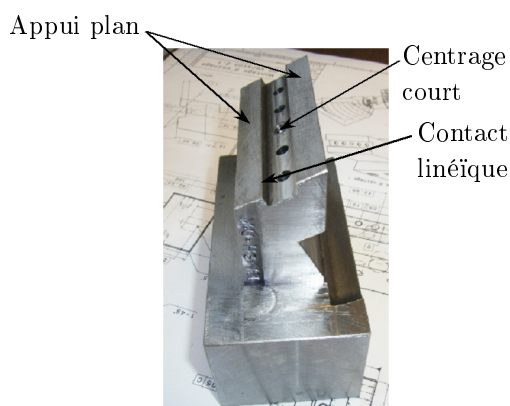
Interface pale / montage d'usinage sur le montage d'usinage.
